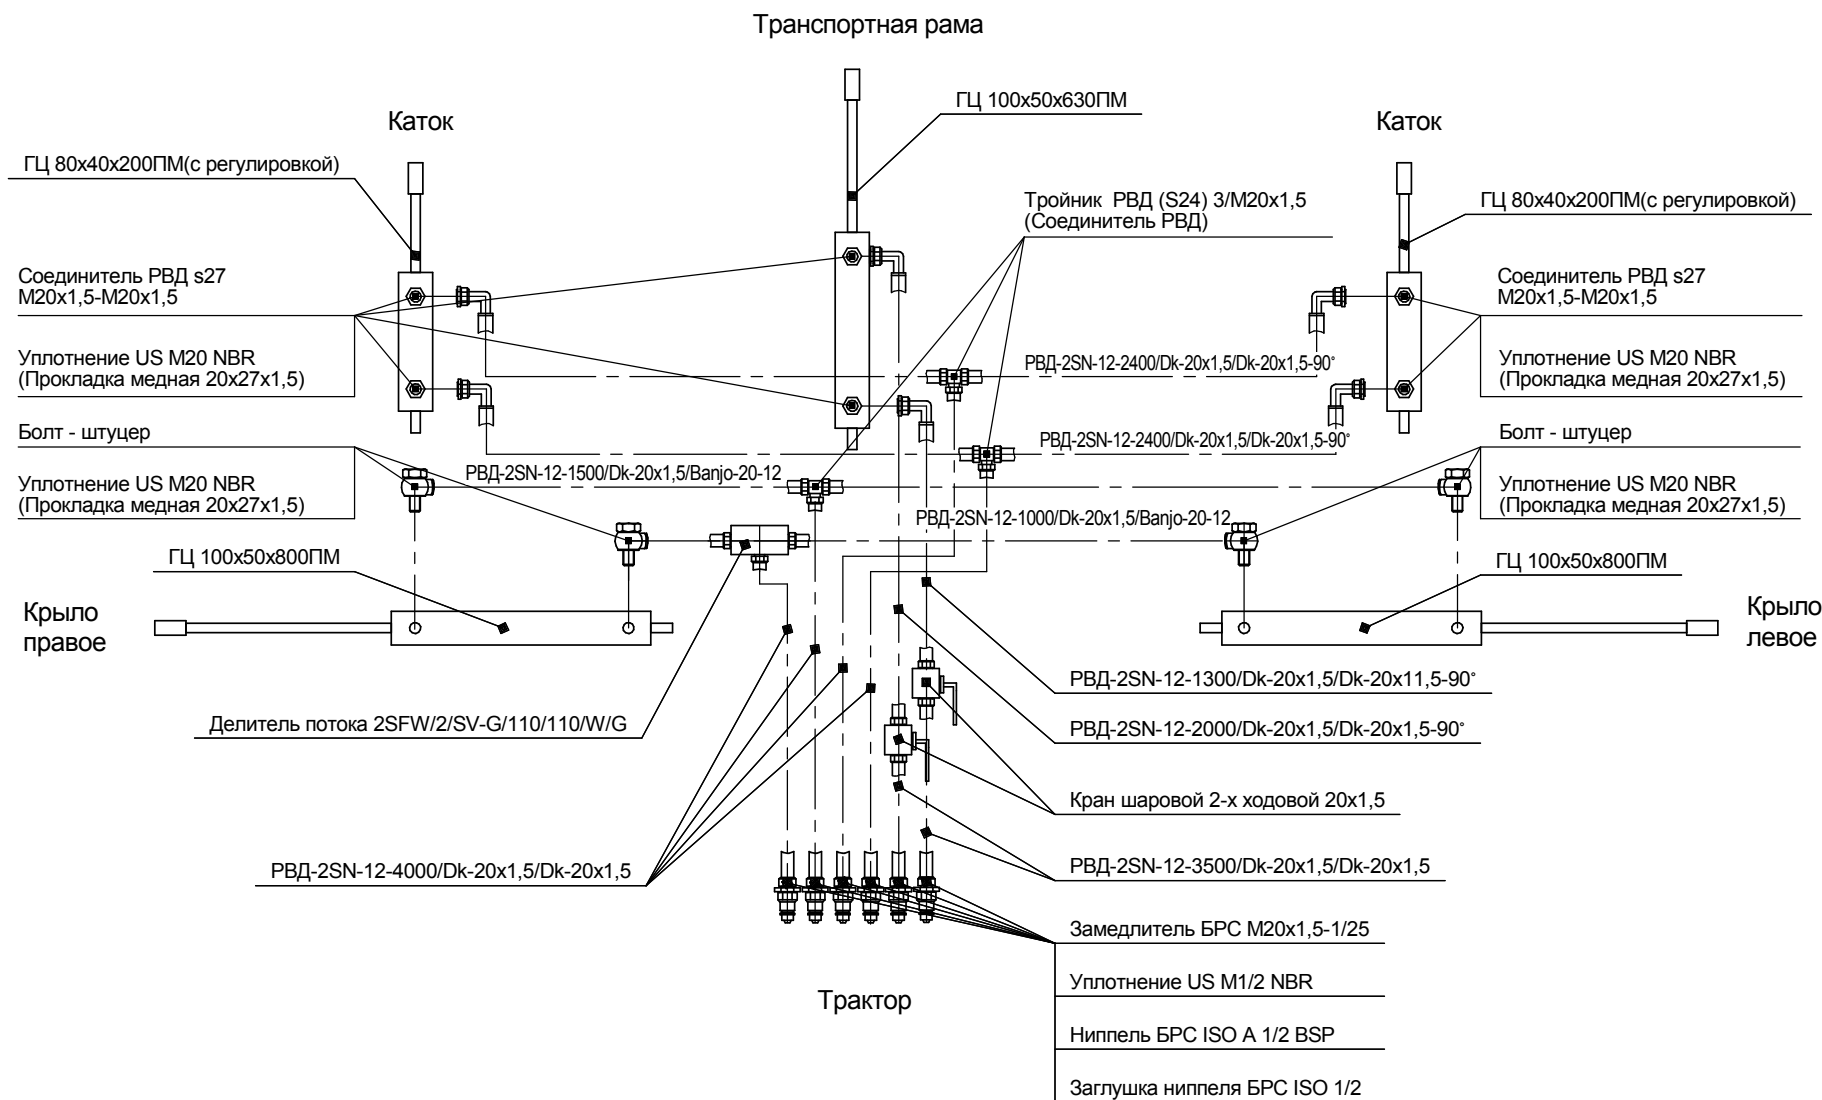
Схема гидравлическая дисковая почвообрабатывающая машина ДГМ-7500 "Универсал" / "Универсал Т"
